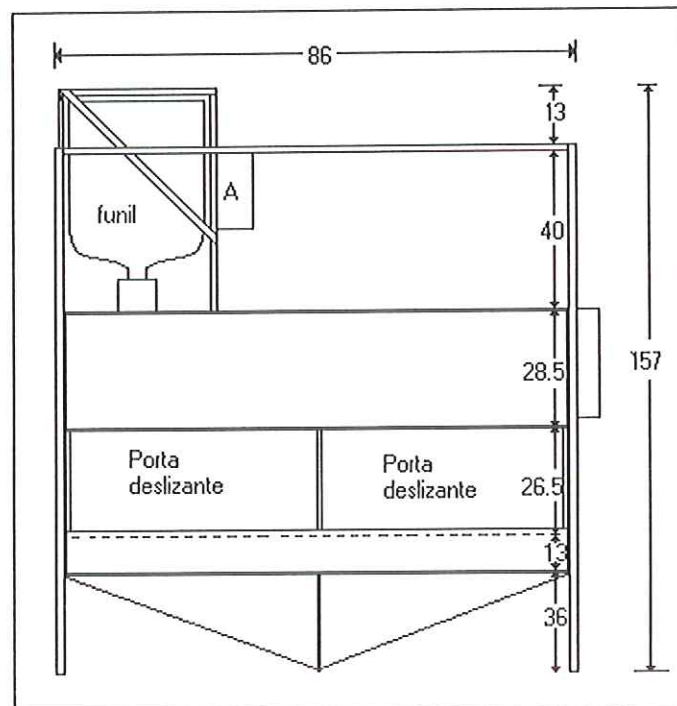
Desenho da face frontal da caixa com dimensões.
